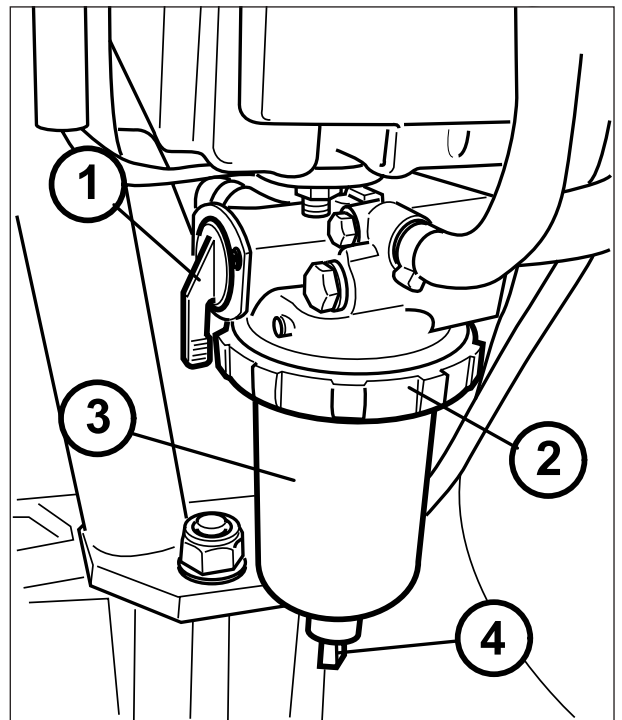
Pre-filtro combustible (9045 - 9055)
